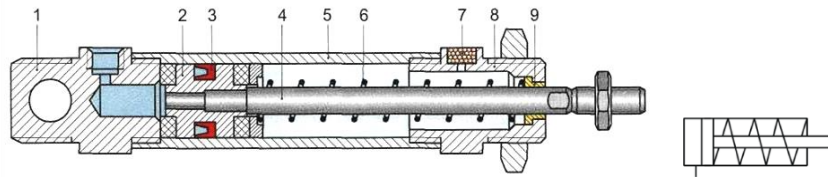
Пневмоцилиндр одностороннего действия: 1 – задняя крышка; 2 – поршень; 3 – уплотнение; 4 – шток; 5 – корпус; 6 – пружина; 7 – отверстие с фильтром; 8 – передняя крышка; 9 – направляющая втулка
